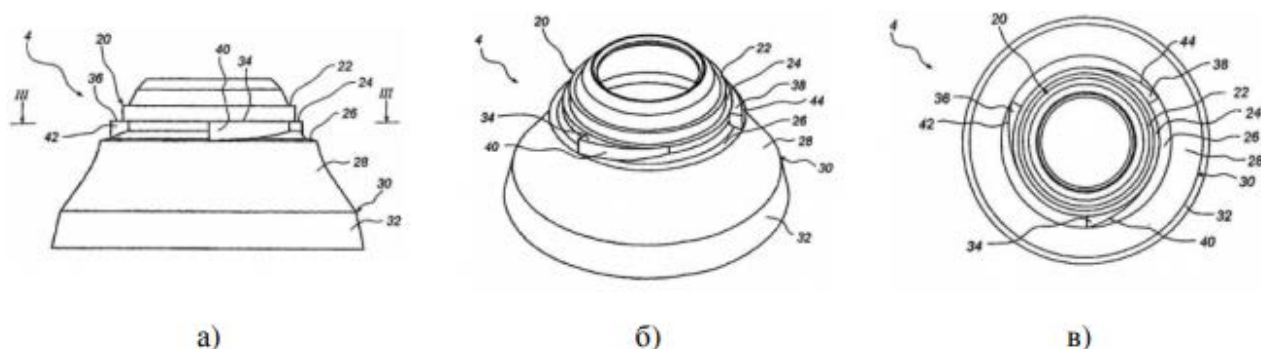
Схеми внутрішнього корпусу рухомого конуса а) вигляд збоку; б) ізометрична проекція; в) вигляд зверху
